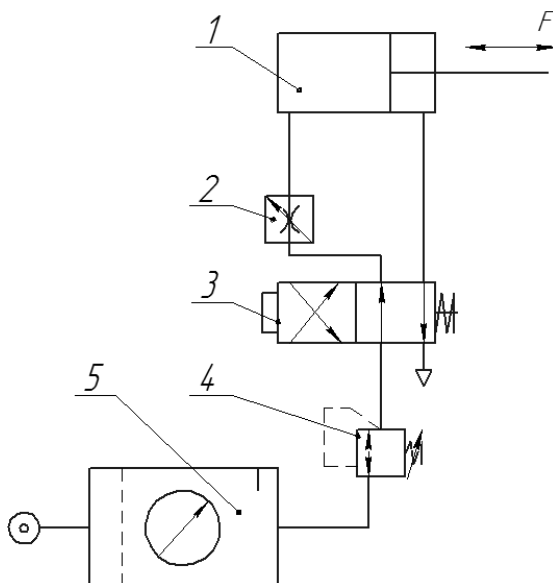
Пневматическая система механизма поштучной подачи (1- пневмоцилиндр; 2-пневмодроссель; 3- пневмораспределитель; 4- предохранительный клапан давления; 5- блок подготовки сжатого воздуха)
